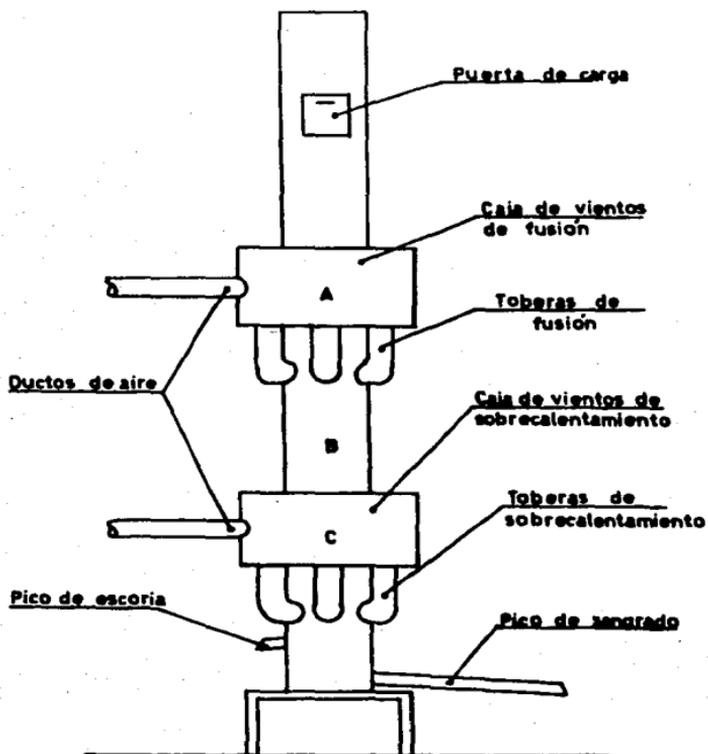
Cubilot Irlandés, vista de planta y elevación.
